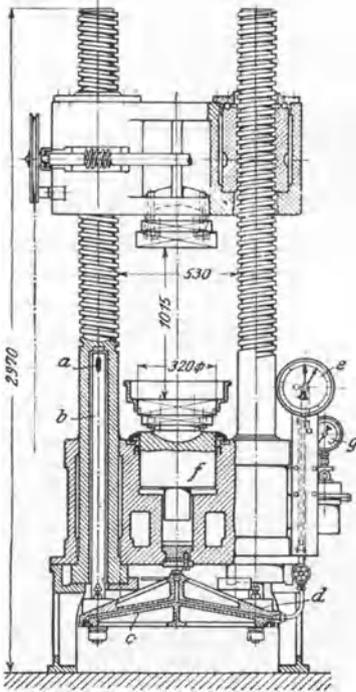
Hydraulische Presse mit Kraftmesser durch Säulendehnung von Amsler (Schnittzeichnung).
